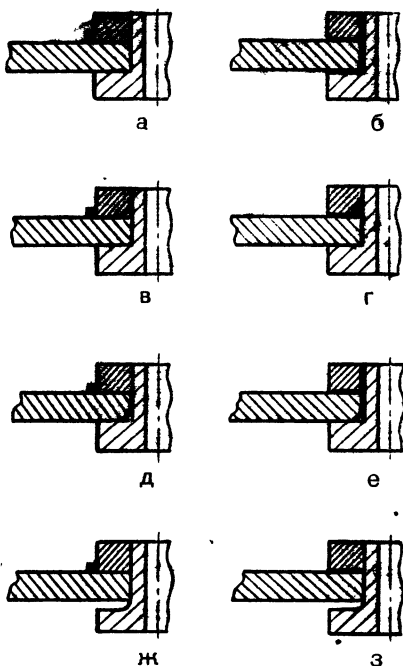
Конструкции сварных соединений герметичных корпусов:
